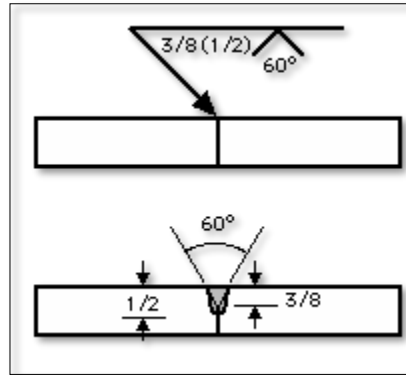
Profundidad de soldadura mayor que la profundidad del canal.
